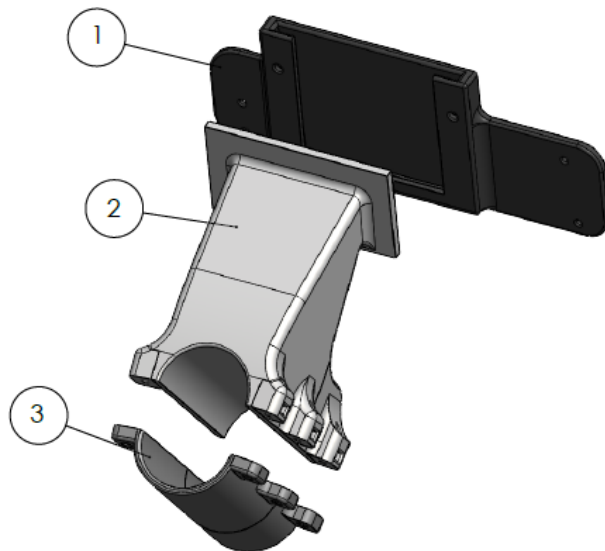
Vista explosionada del anclaje, cuerpo y envoltura.
